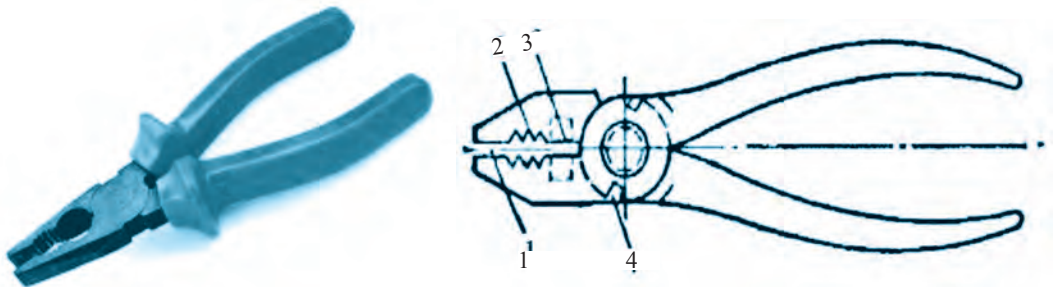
Слесарные щипцы: 1 – плоская сдавливающая часть; 2 – дуговидная часть, предназначенная для прочного удержания вещей цилиндрической формы; 3 – режущие лезвия; 4 – маленькое углубление для резки проволоки с круглым сечением.
